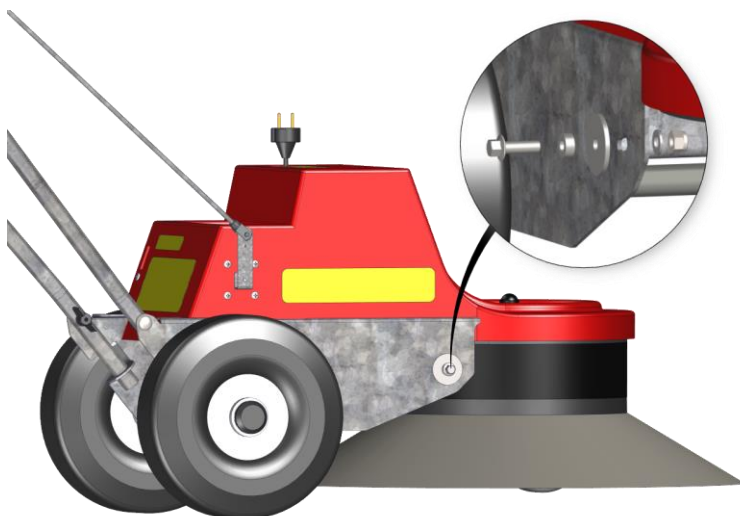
Aufnahmeschraube Schwadblech WR 650
